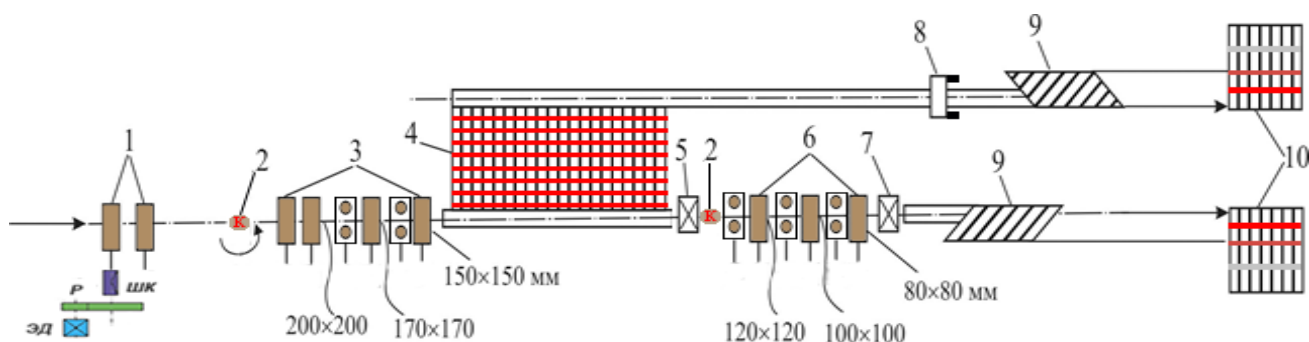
Непрерывно-заготовочный стан 900/700/500
